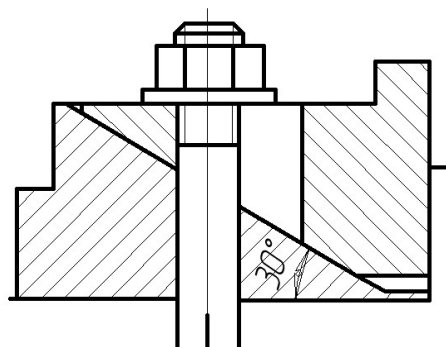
Схема клинового механізму для передавання зусилля затиску
